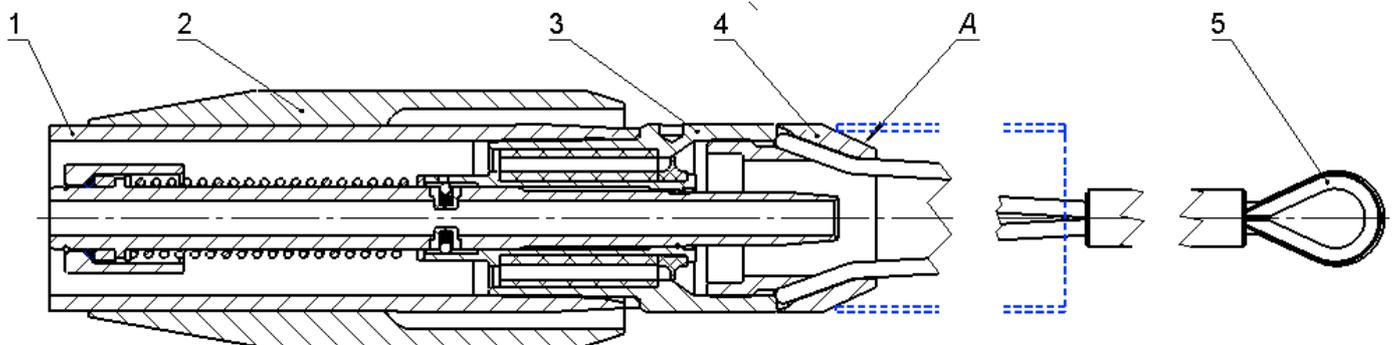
Схема сборки пробойника для протяжки труб (по заказу) :
